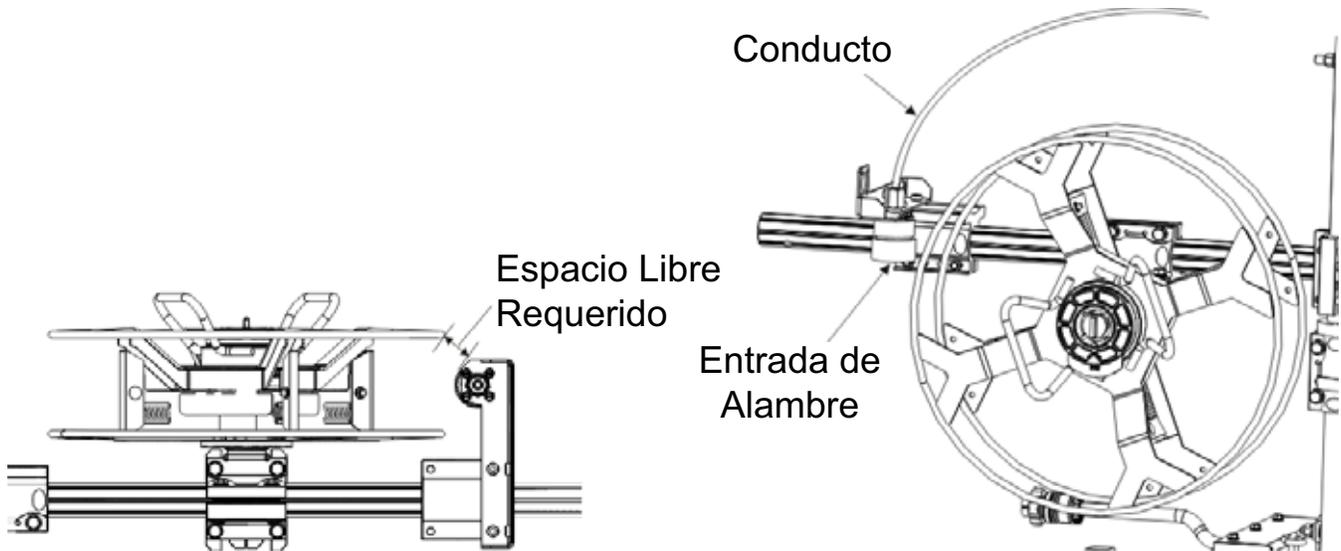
B – MONTAJE DE LA CUBIERTA
